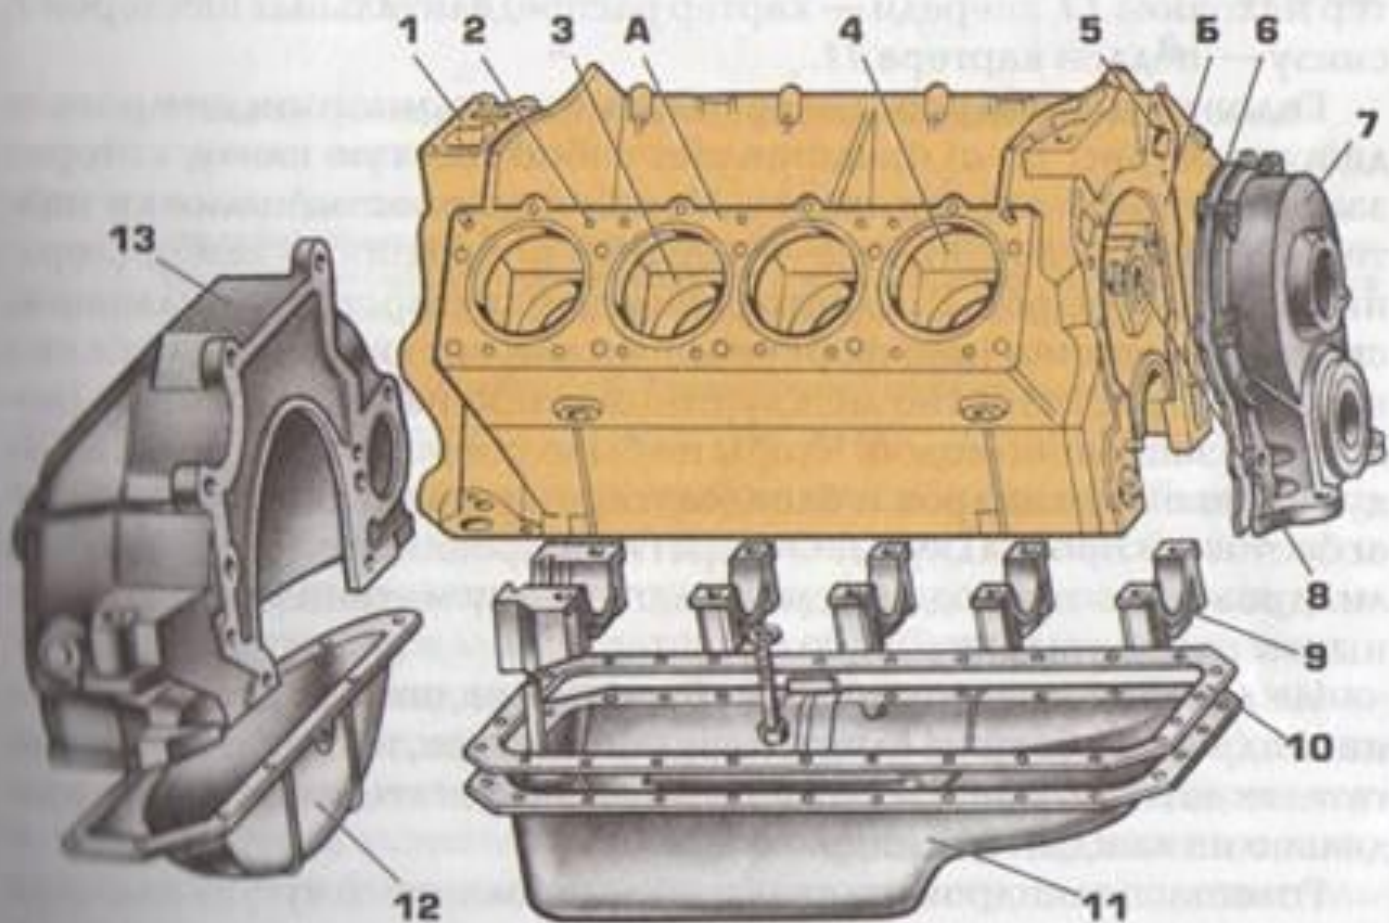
Корпусные детали двигателя ЗИЛ-508:
